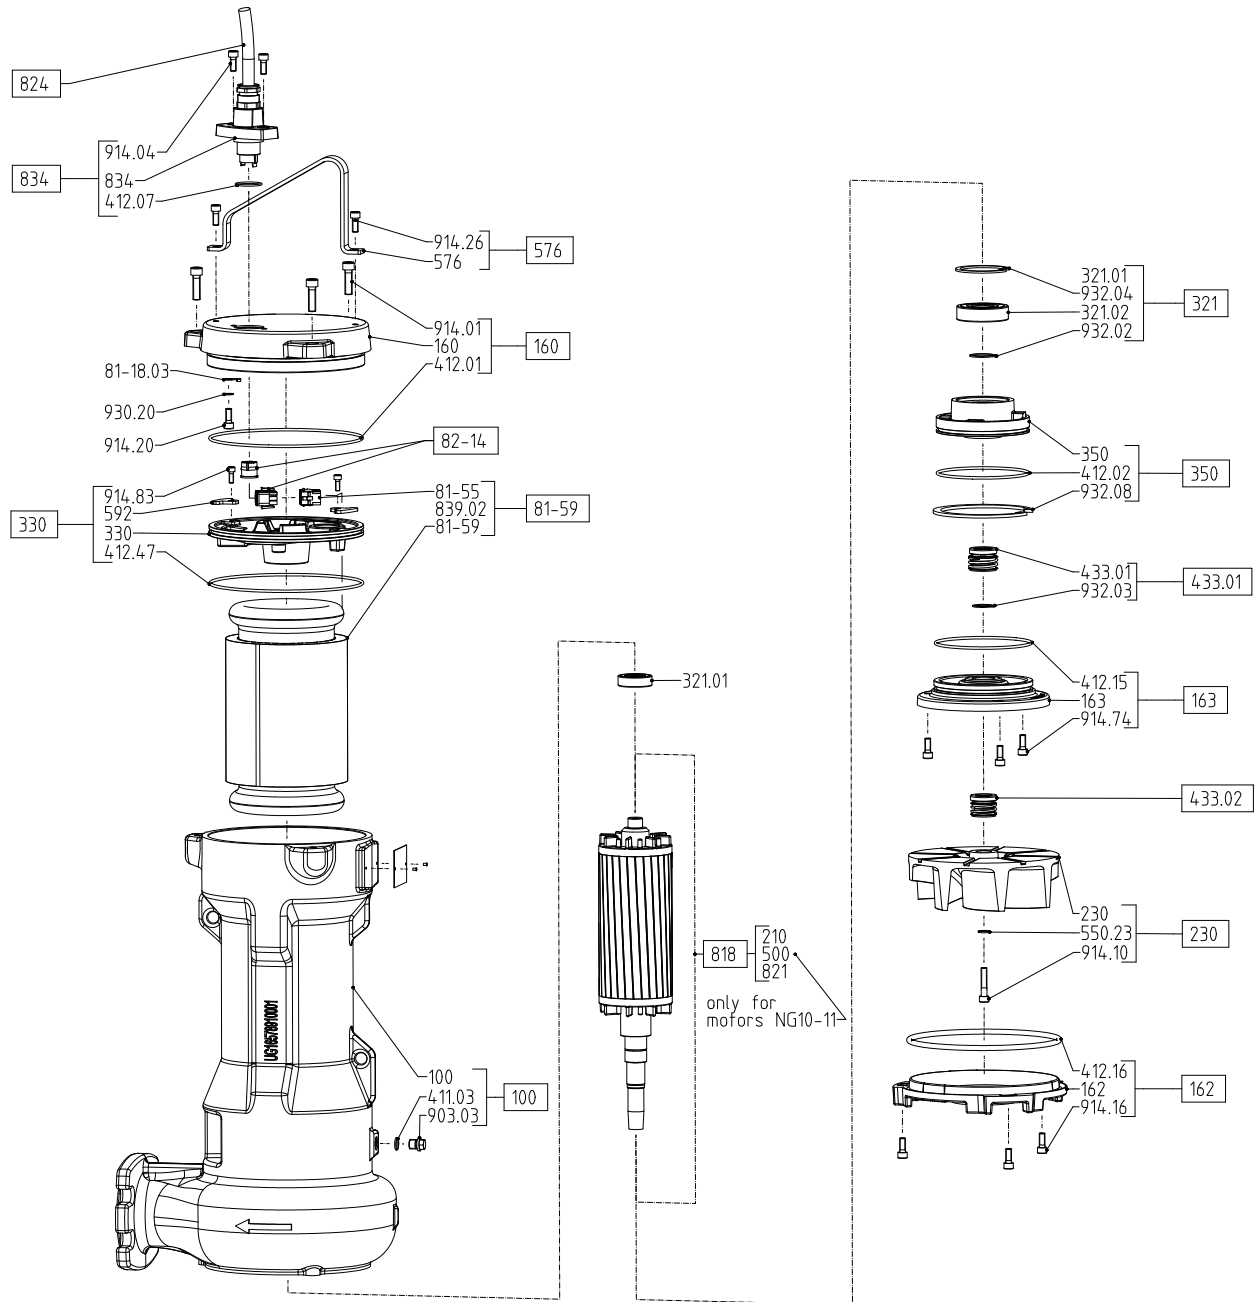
Explosionszeichnung Amarex D-max, Ausführung US
